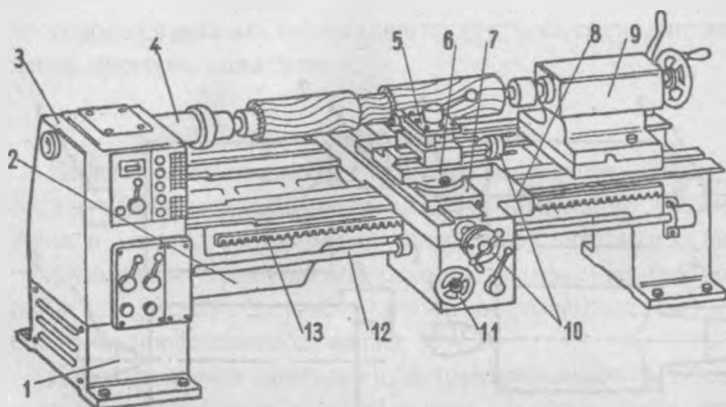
Токарный станок с механической подачей суппорта и приставным лобовым устройством ТС-40:
